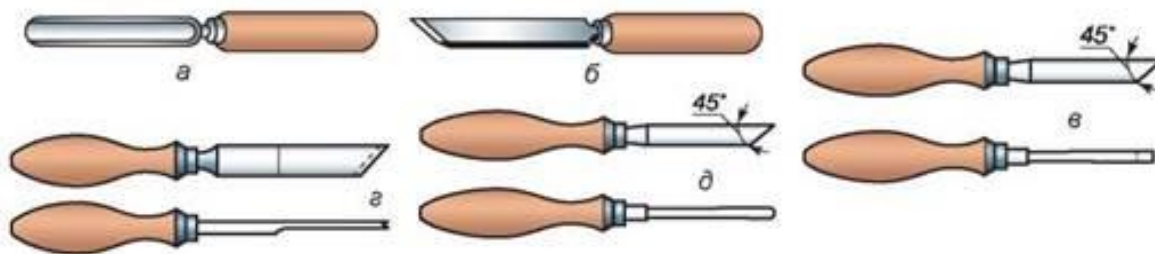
Різальні інструменти для токарних робіт: а - реєр; б - мейсель; в - канавочник прямий; г - відрізний різець; д - канавочник напівкруглий
